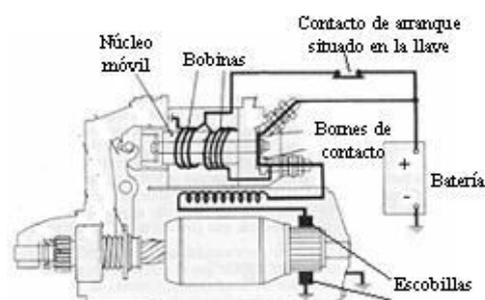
PARTE ELÉCTRICA DEL MOTOR DE ARRANQUE CON SOLENOIDE INTEGRADO
